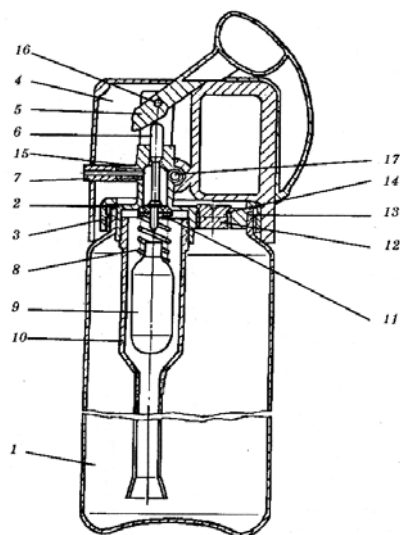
Будова вогнегасника ОП-1В «Момент-2»: 1 – корпус; 2 – головка; 3 – гайка накидна; 4 – ковпак; 5 – важіль запуску й керування клапаном; 6 – голка; 7 – насадок-розпилювач; 8 – пружина; 9 – балон з робочим газом; 10 – лгрубка сифонна; 11 – клапан; 12 – пробка; 13 – кільце ущільнювальне; 14 – кільце ущільнювальне; 15 – кільце ущільнювальне; 16 – вісь; 17 – гвинт
